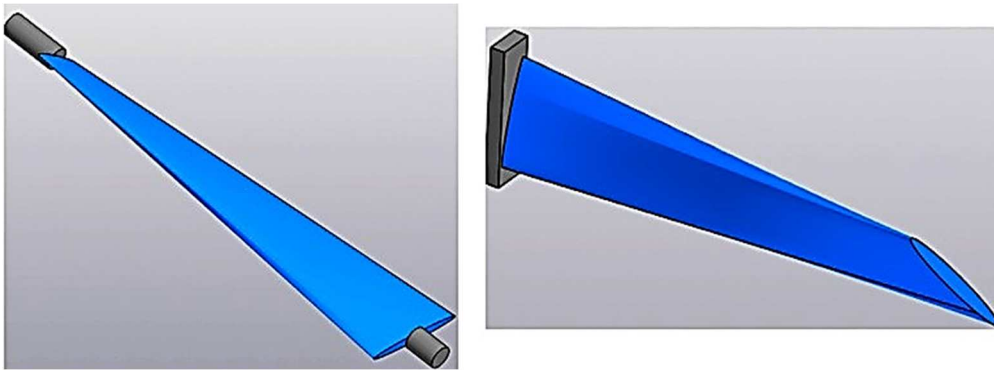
Поворотные и рабочие лопатки компрессора
